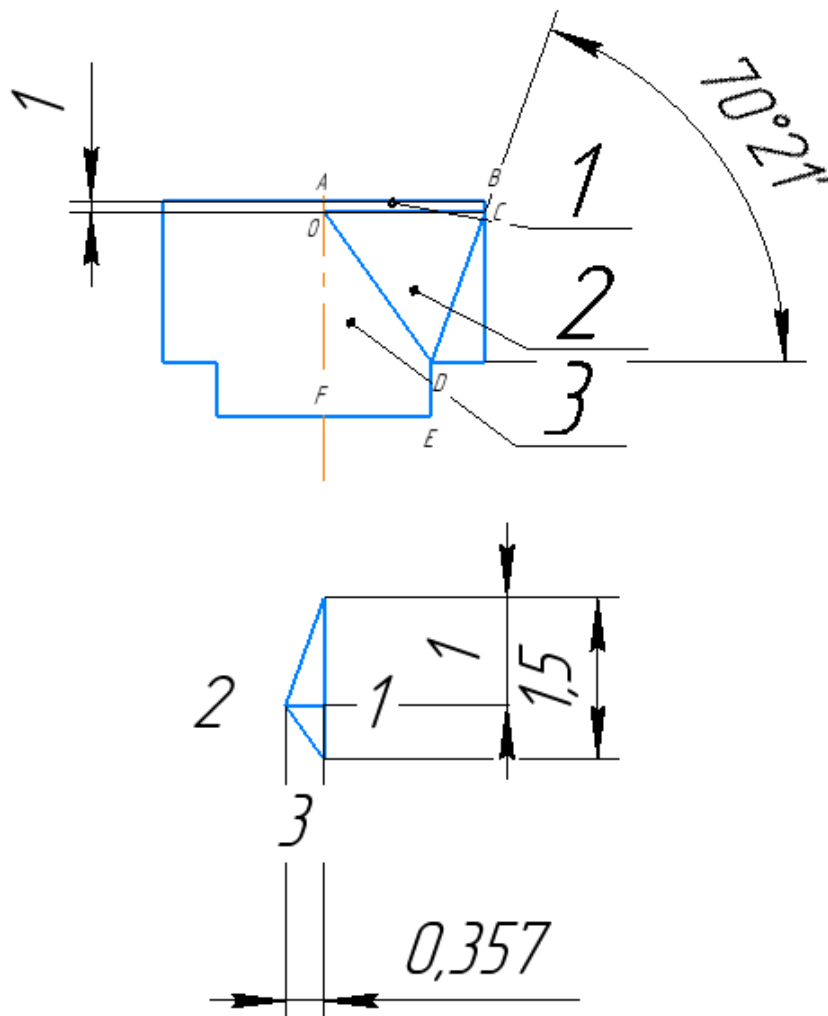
Розрахункова схема 5 (кут 70) та план швидкостей до розрахункової схеми
